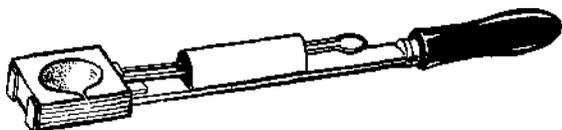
Приспособление для удержания шамотной или асбестовой плиты (тигелька) в процессе ручной плавки и отливки
